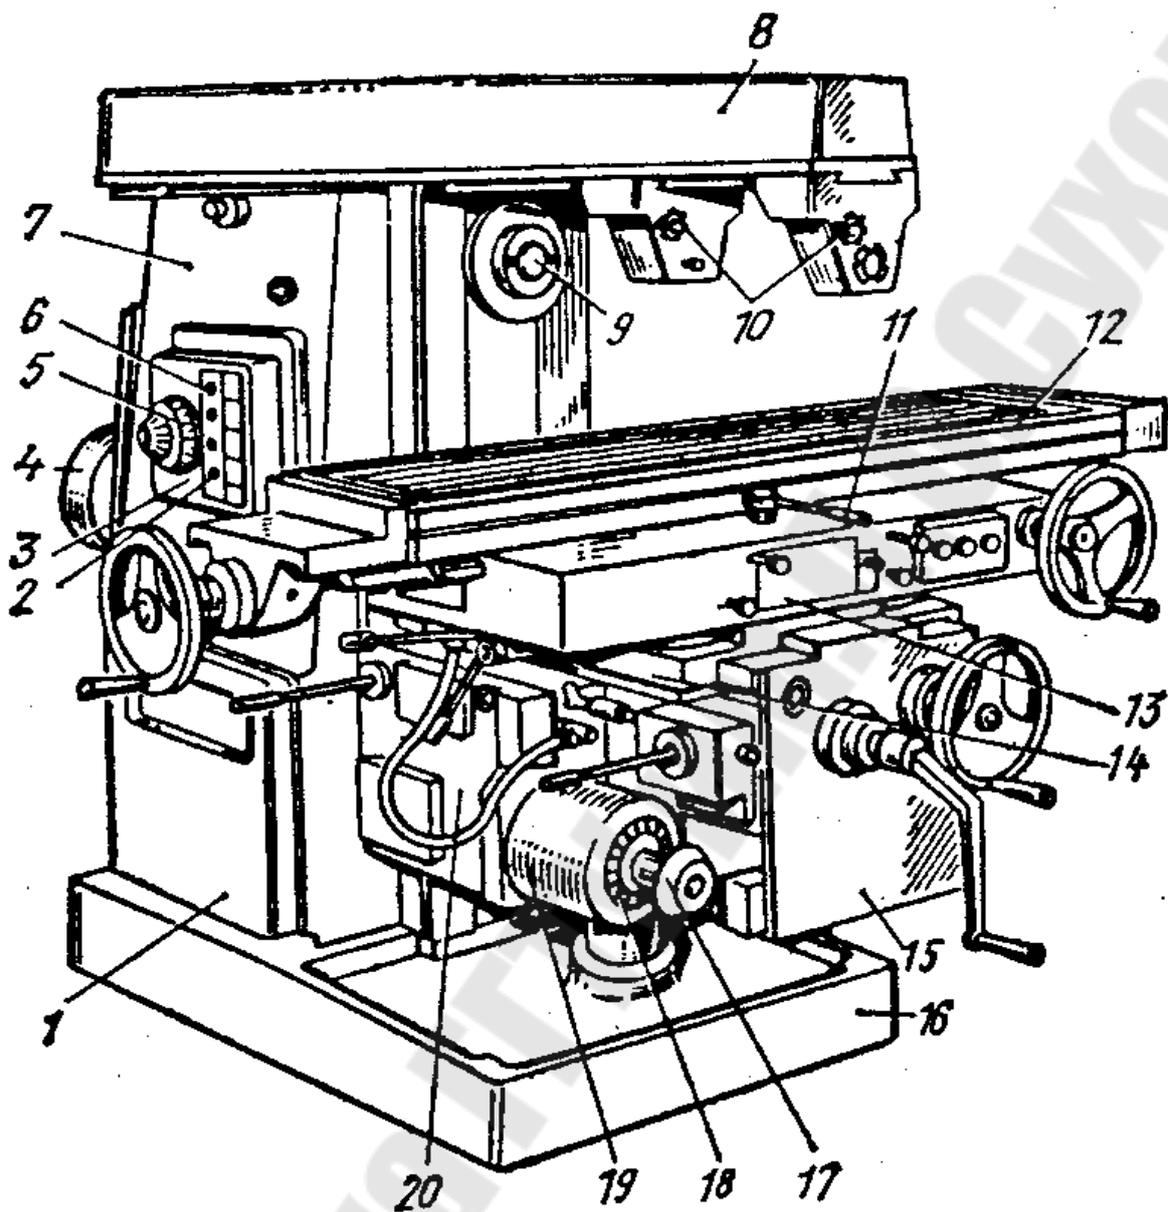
Общий вид горизонтально-фрезерного консольного станка
